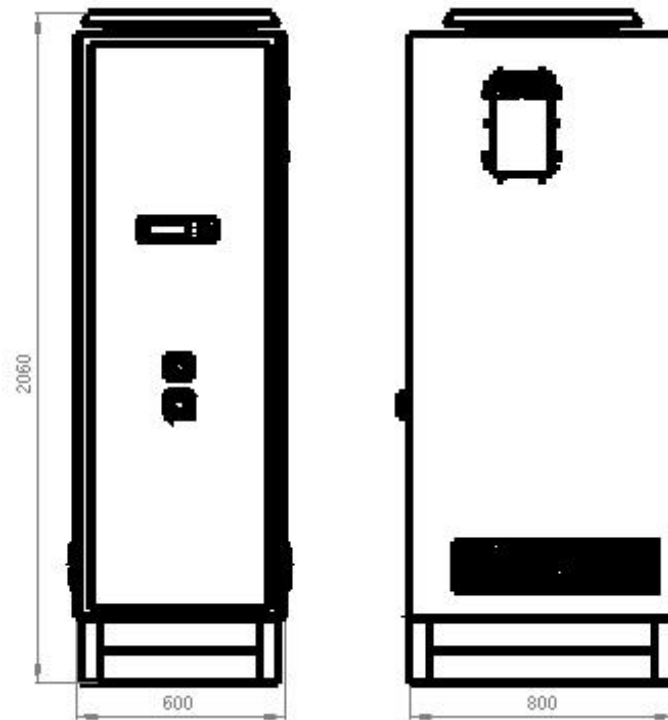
Габаритные и присоединительные размеры зарядного устройства
